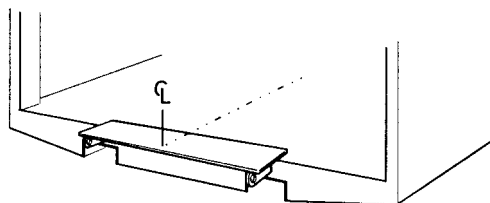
Mittelpunkt an der Hecktraverse des Fahrzeugs ausmessen und Montage durchführen. Die Montagevorrichtung an der Hecktraverse anschrauben oder durch Punktschweißen befestigen
